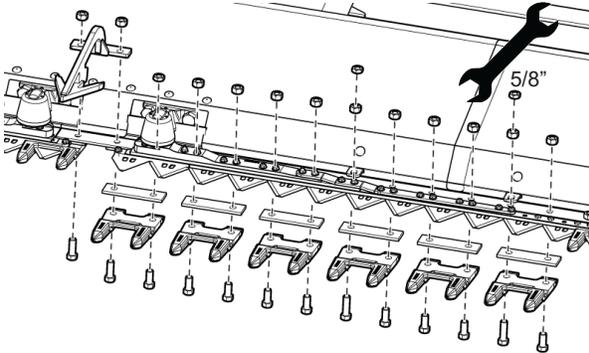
Retire las protecciones de alrededor de la cabeza de la cuchilla izquierda
